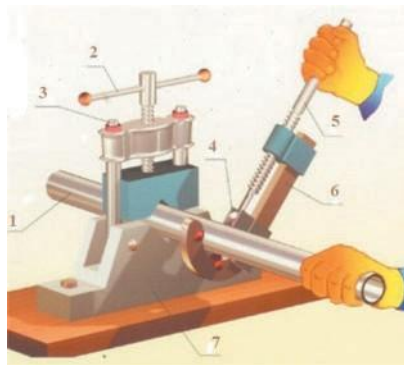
Труборіз: 1 – труба, 2 – рукоятка, 3 – гвинт, 4 – рухомий ролик, 5 – рукоятка труборіза, 6 – труборіз, 7 – притиск
